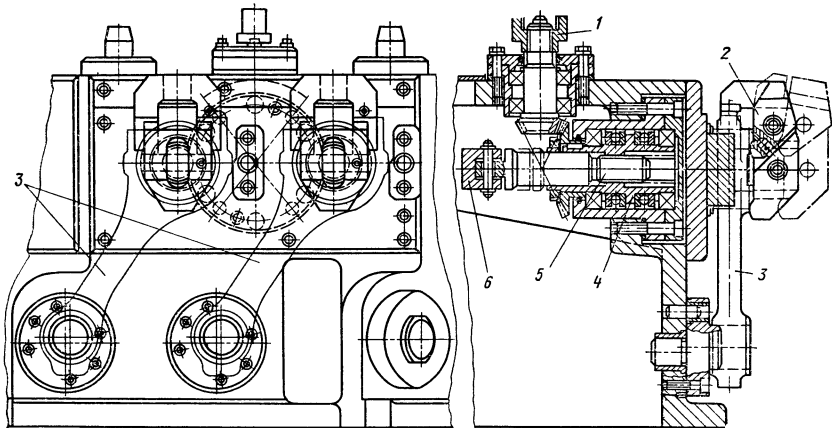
Позиция поворотного приспособления для обработки шатунов:
